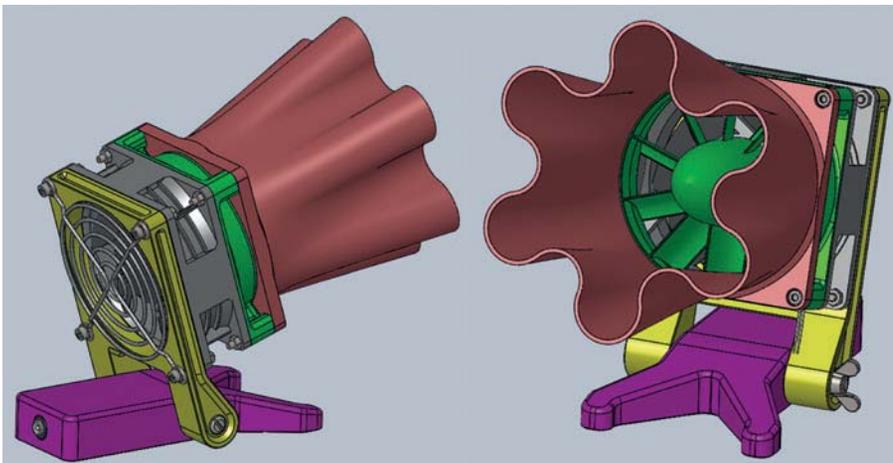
Kleiner Ventilator mit 80 mm Durchmesser
